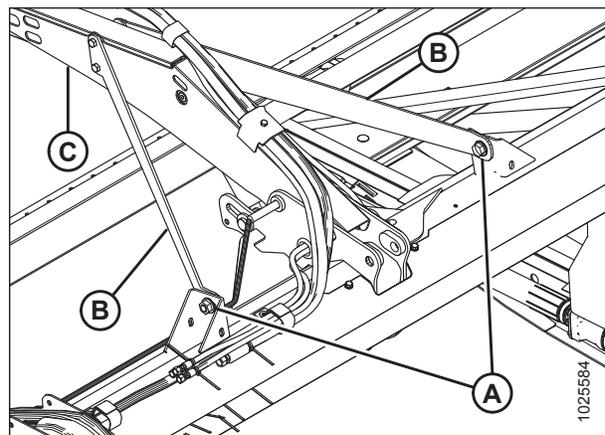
Стяжки центрального опорного рычага мотвила – Северная Америка
